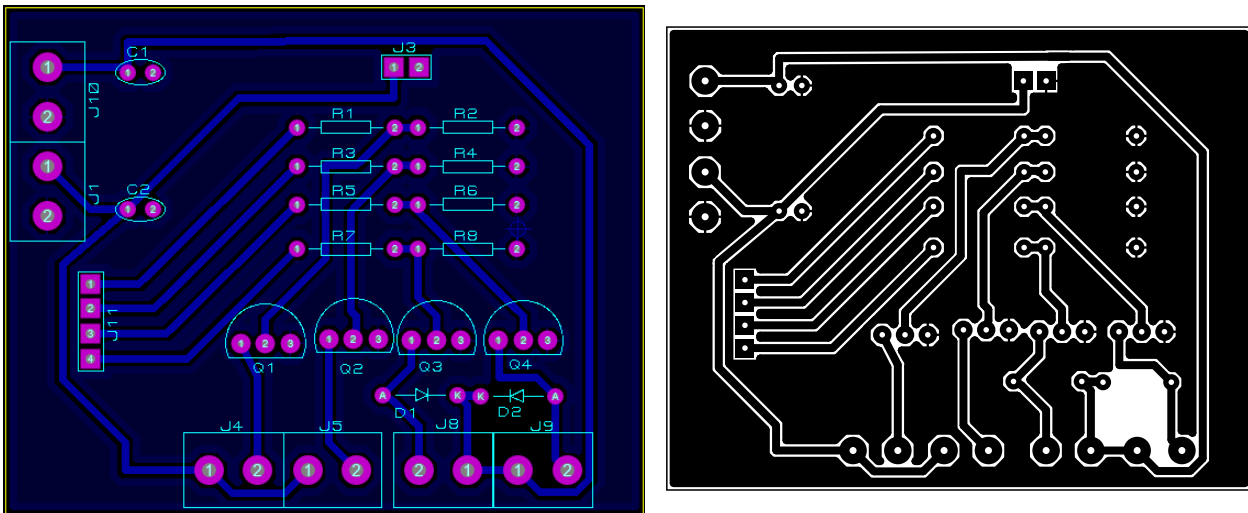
Izquierda PCB ARES. Derecha negativo para insoladora
